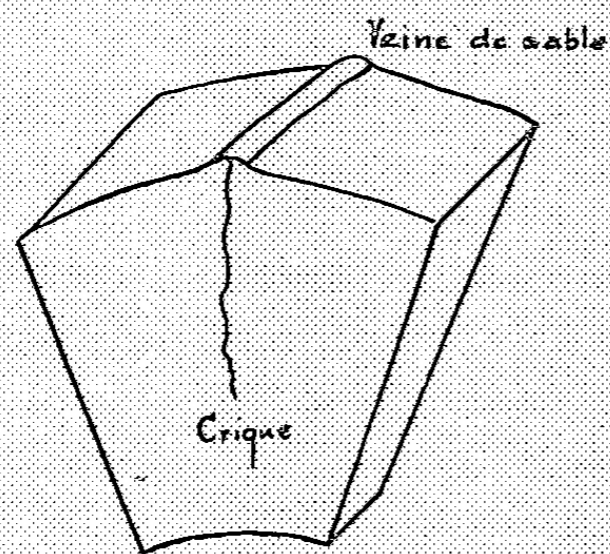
Crique soudée par apport de métal liquide et débouchant dans une veine de sable et d'acier.
